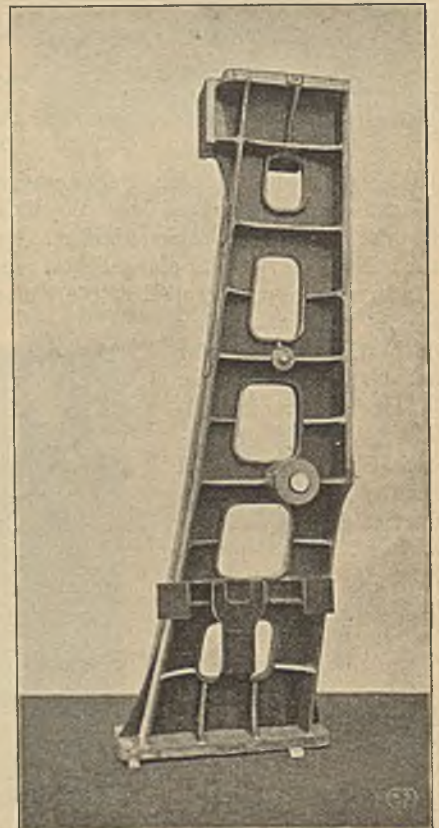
Maschinenständer für einen Lloyd-Dampfer, 4,66 m hoch, 4000 kg.
